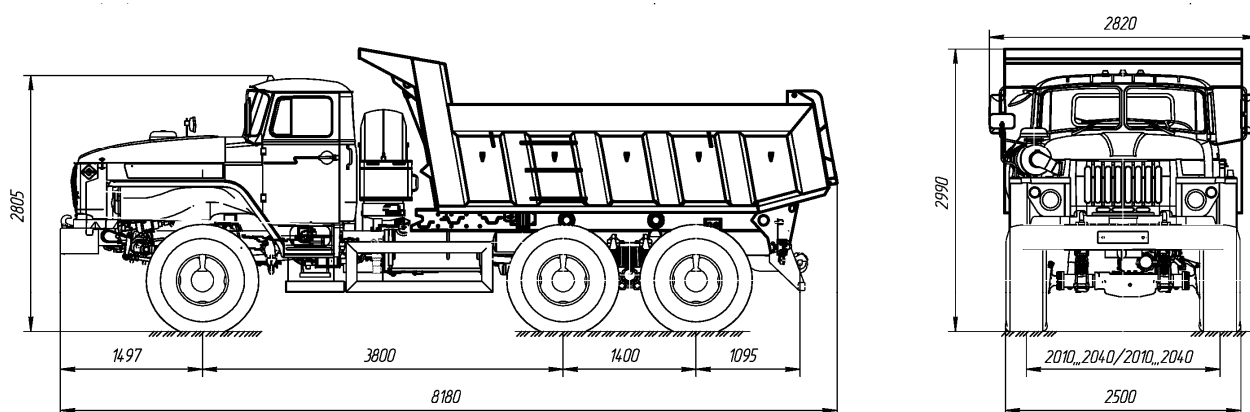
Габаритные размеры автомобиля-самосвала Урал-55571-0000121-72/60 с платформой ковшового типа $V=8 \text{ м}^3$ с задним бортом (возможно исполнение без заднего борта)
